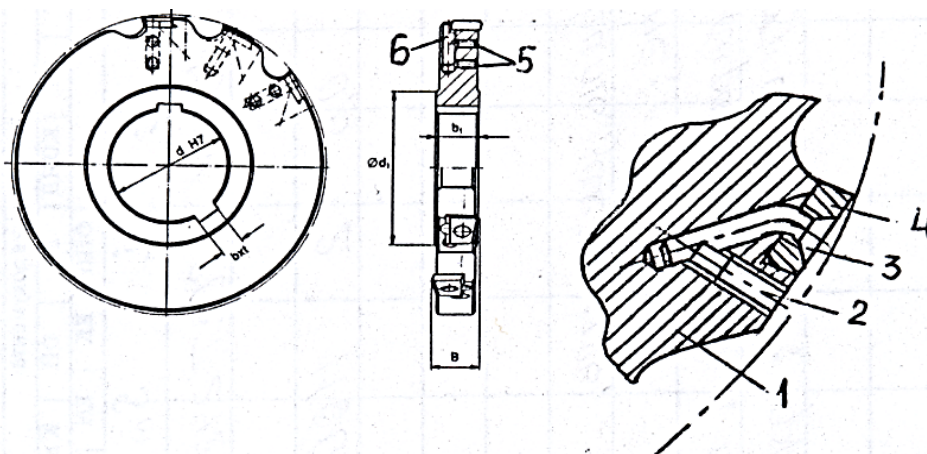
Конструкция сборной дисковой трехсторонней фрезы 133/2
